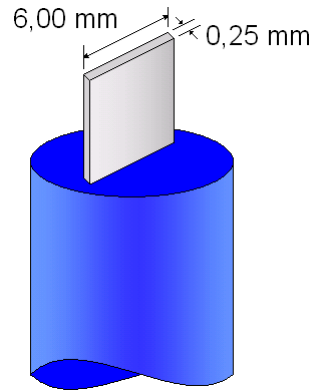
Detalhe da seção transversal da barra interna do modelo.
